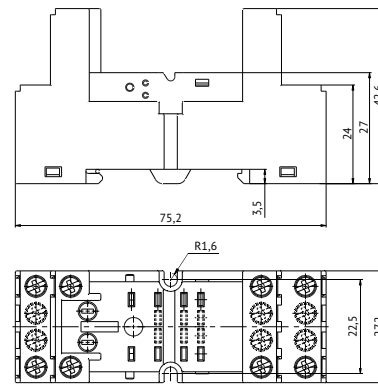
Габаритные, установочные, присоединительные размеры розеток OptiRel G RR94-8X
